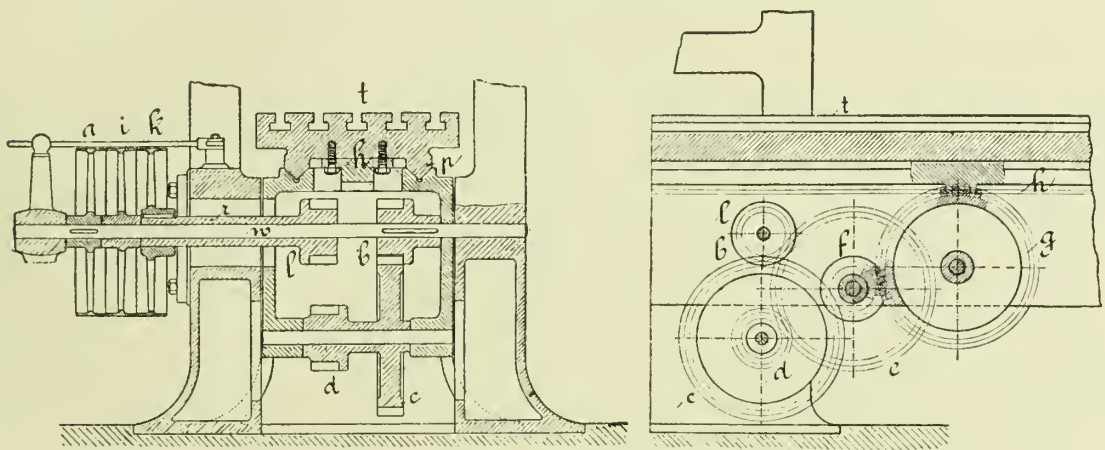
Zahnstangenantrieb einer Hobelmaschine.
